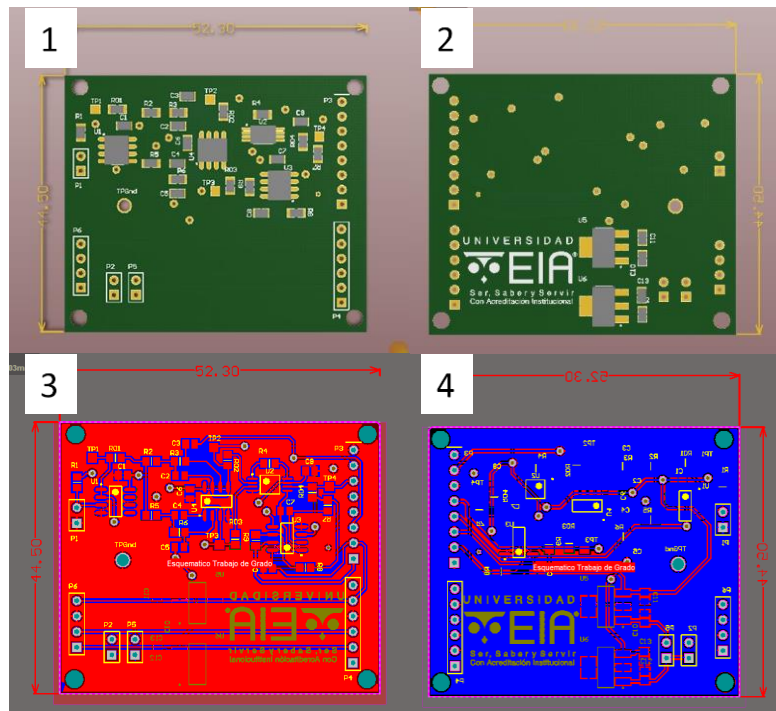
Diseño PCB del dispositivo electrónico realizado en Altium Designer. 1. cara superior de la tarjeta diseñada en 3D. 2. cara inferior de la tarjeta diseñada en 3D. 3. cara superior de la tarjeta diseñada en 2D. 4. cara inferior de la tarjeta
